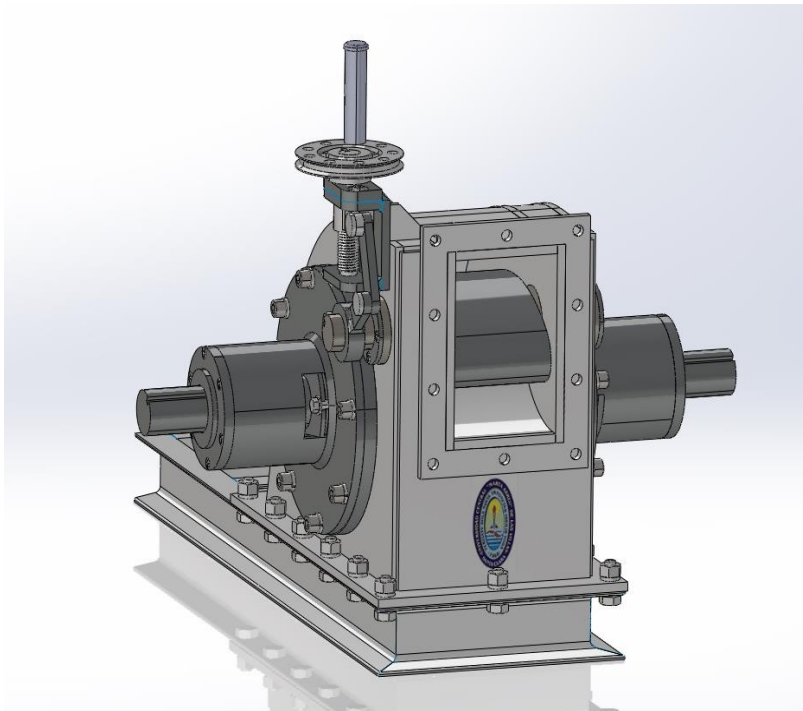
Turbina Michell- Banki diseñada vista frontal izquierda
